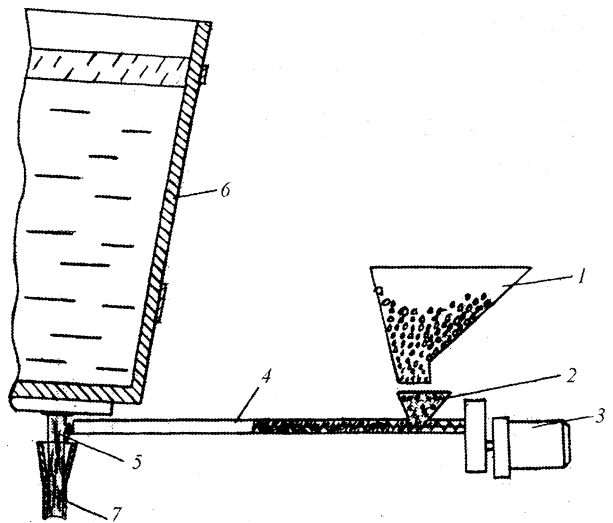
Установка для модифицирования стали со шнековым транспортером: 1 – расходный бункер; 2 – приемная воронка; 3 – электродвигатель с редуктором; 4 – шнековый транспортер; 5 – струя металла, вытекающая из ковша; 6 – ковш с металлом; 7 – центровая
